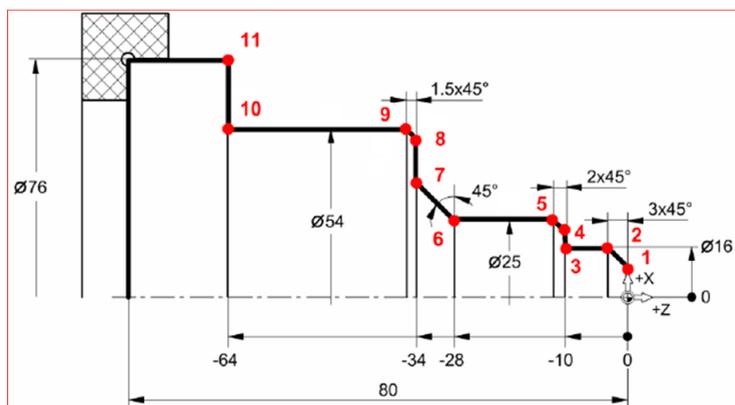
Эскиз детали «вал ступенчатый» [12]
